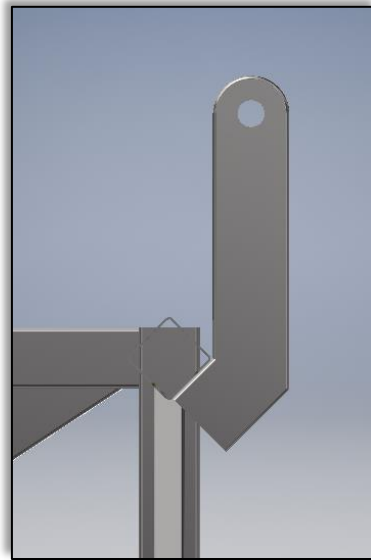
Conformado final de bisagra soldada a estructura
